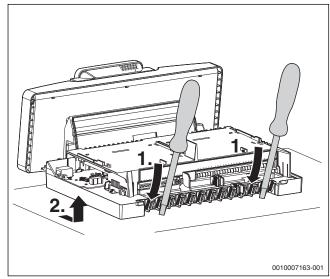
Smontaggio dell'apparecchio di regolazione dalla caldaia
